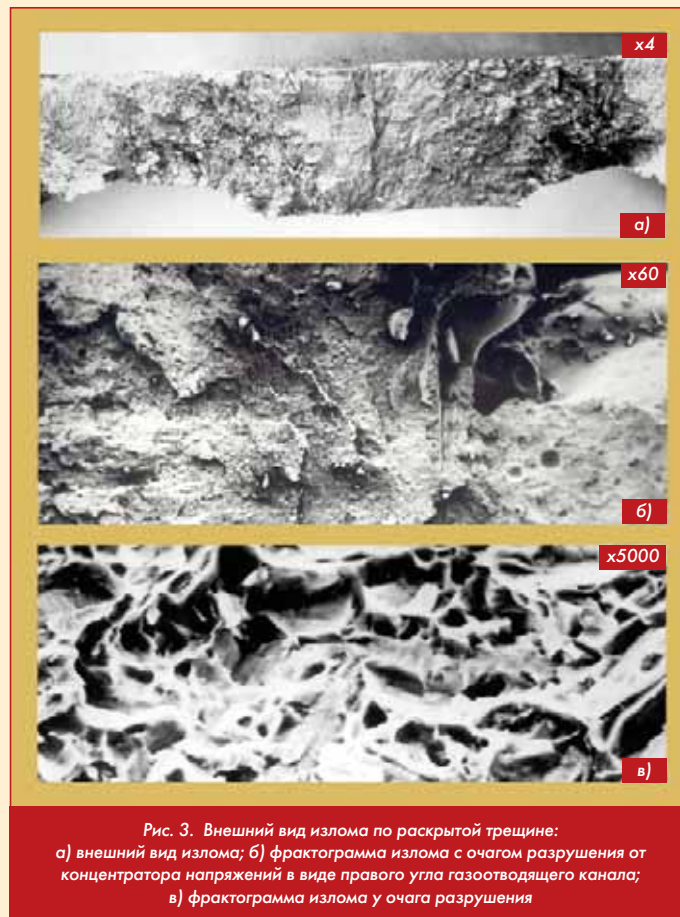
Внешний вид излома по раскрытой трещине:
